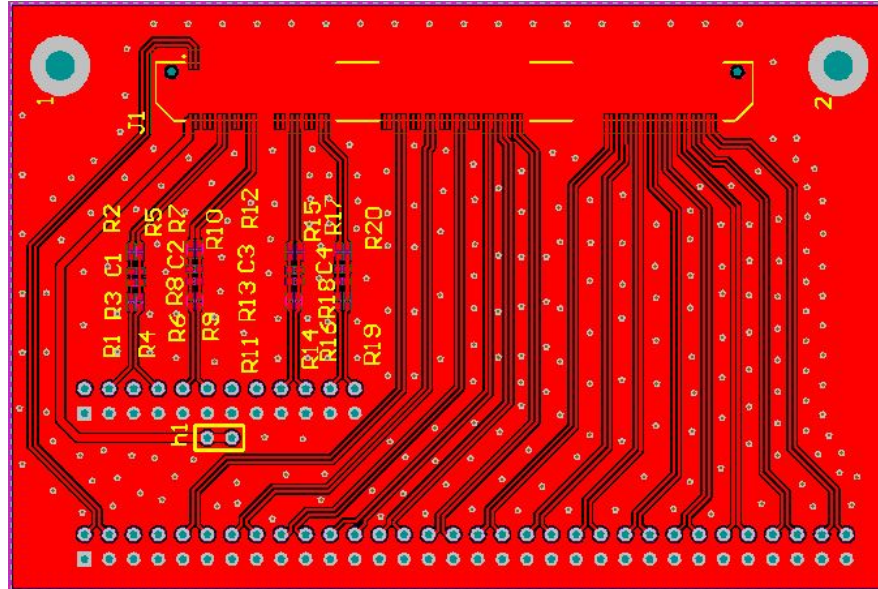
Bottom Layer del connettore posizionato sulla evaluation board.
